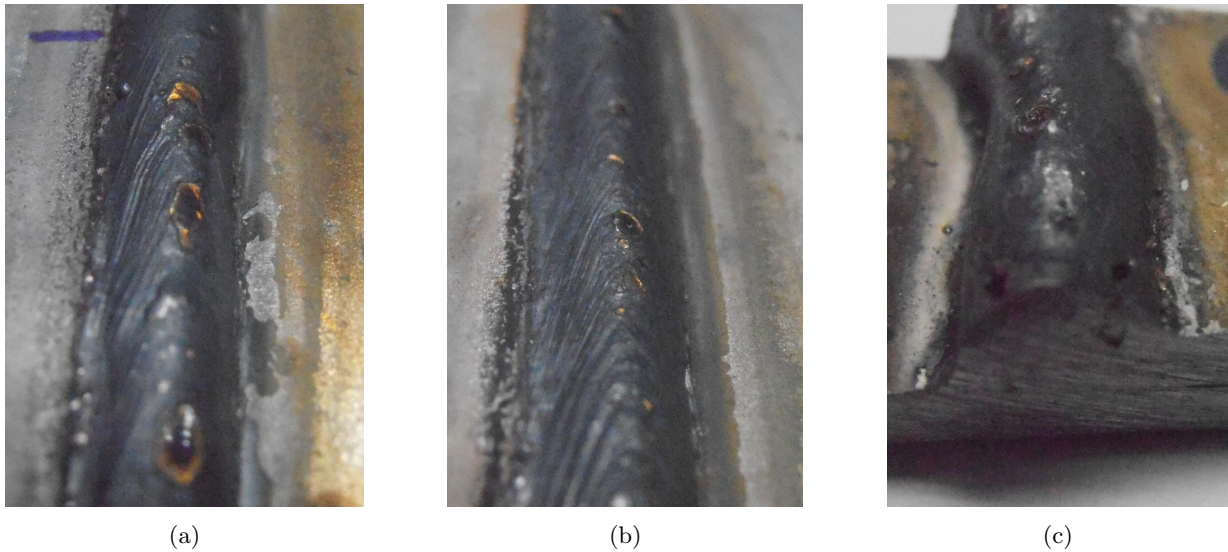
Defectología superficial característica de la soldadura GMAW en los cordones de las muestras soldadas. (a) Inclusiones, (b) aguas y (c) poros.
